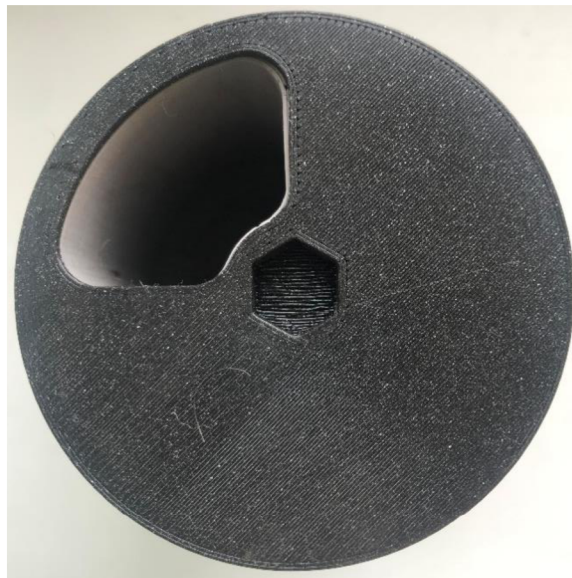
Detail mechanismu pro pohon. Foto autor.
